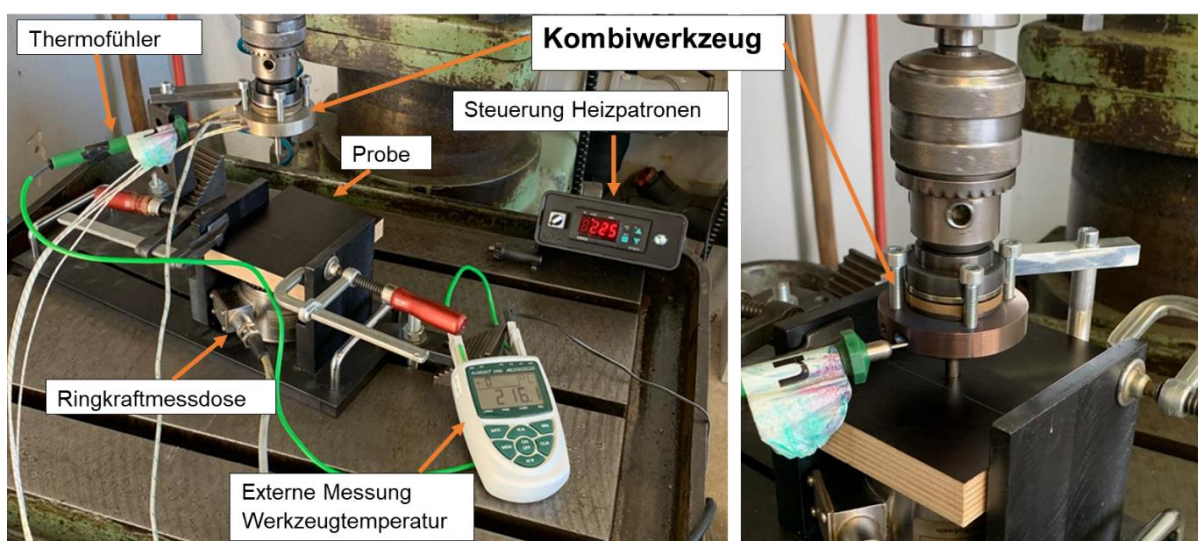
Versuchsaufbau für die Kombiverdichtung auf einer Schwerlast-Standbohrmaschine
